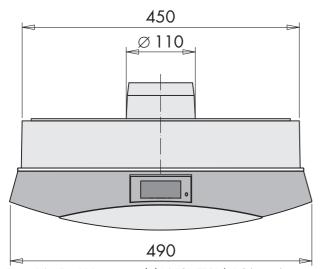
Fig. 11 Dimensions de l'JUNIOR ETW / RDC (en mm)
